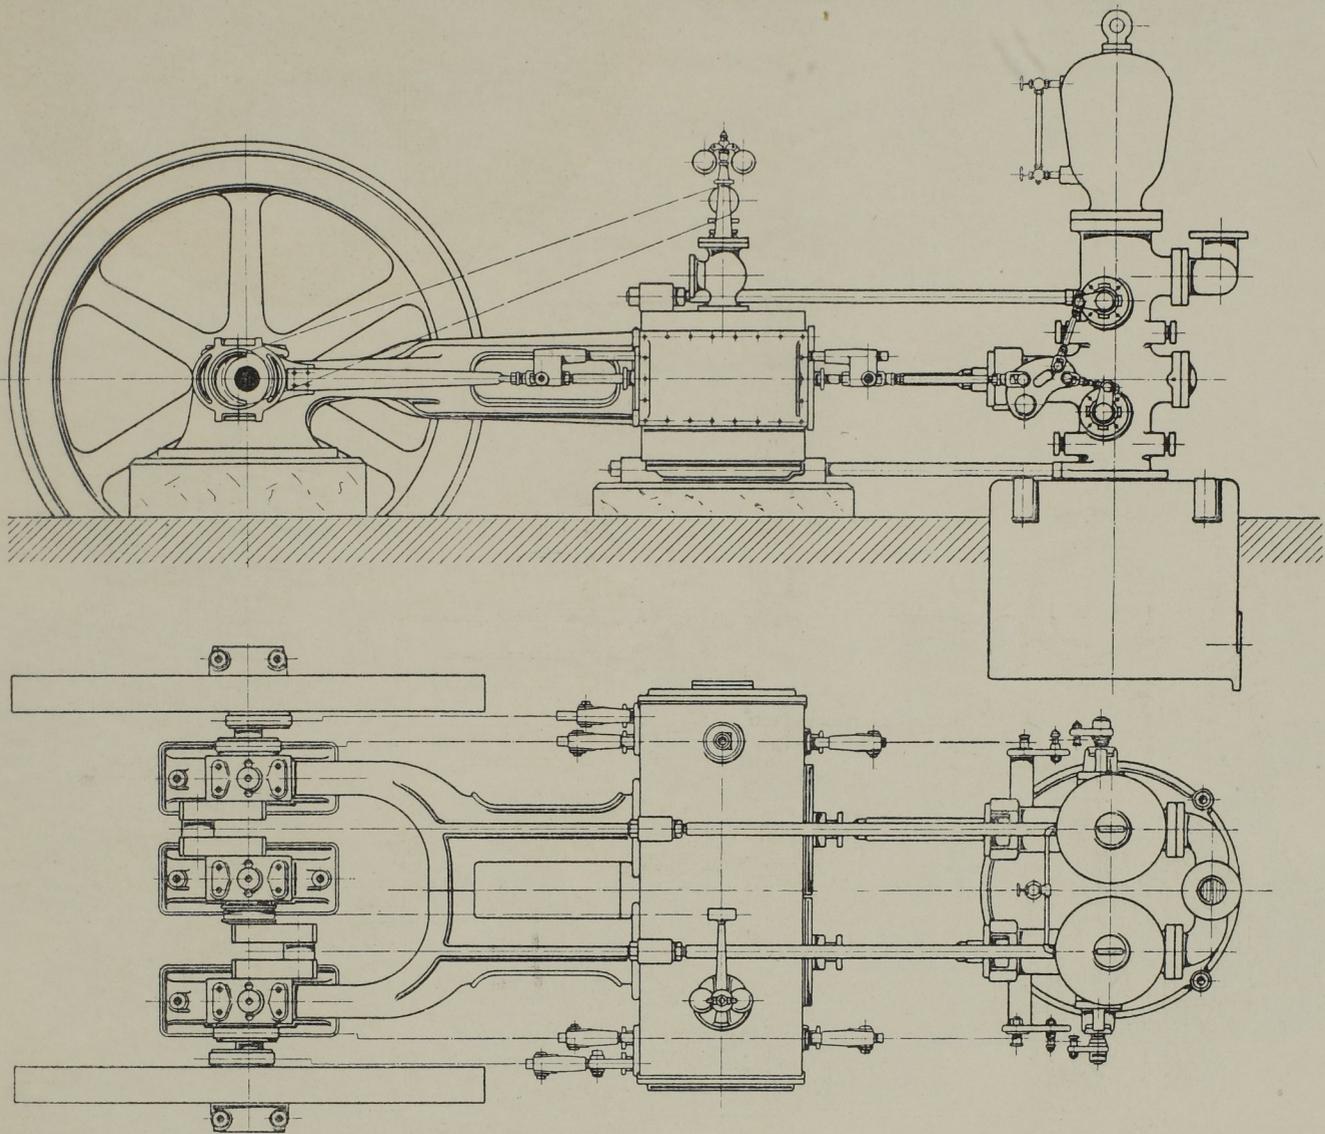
Seitenansicht und Grundriss. Massst. 1:32.
